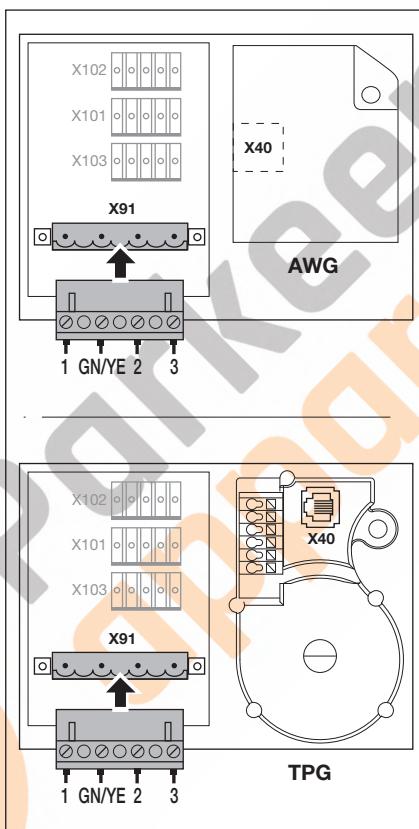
Anschluss der Motorleitung an die Motoranschlussplatine
